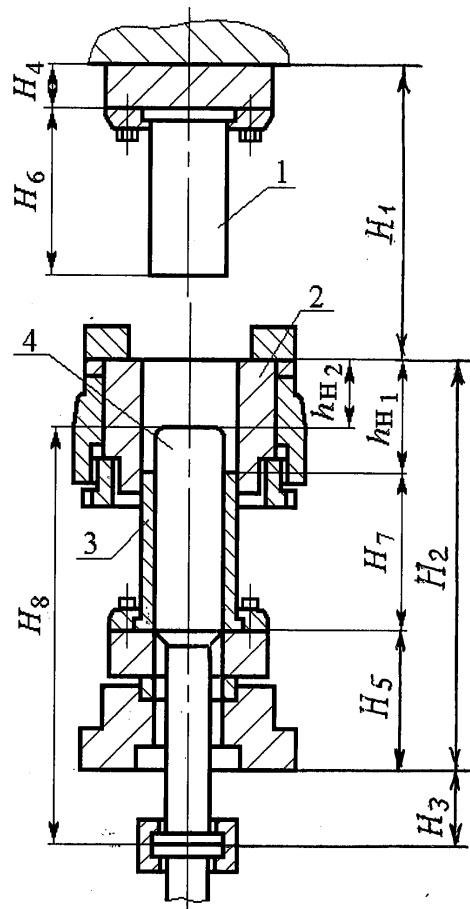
Пресс-форма (штамп) для формирования заготовки стакана
